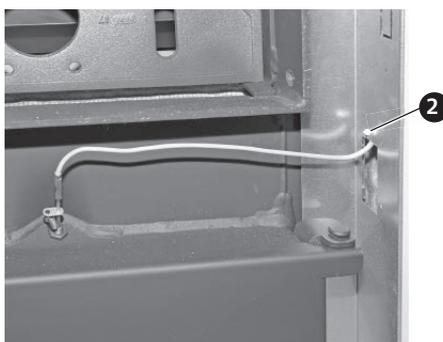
Tirer le câble en arrière et le fixer à l'aide du serre-câbles
